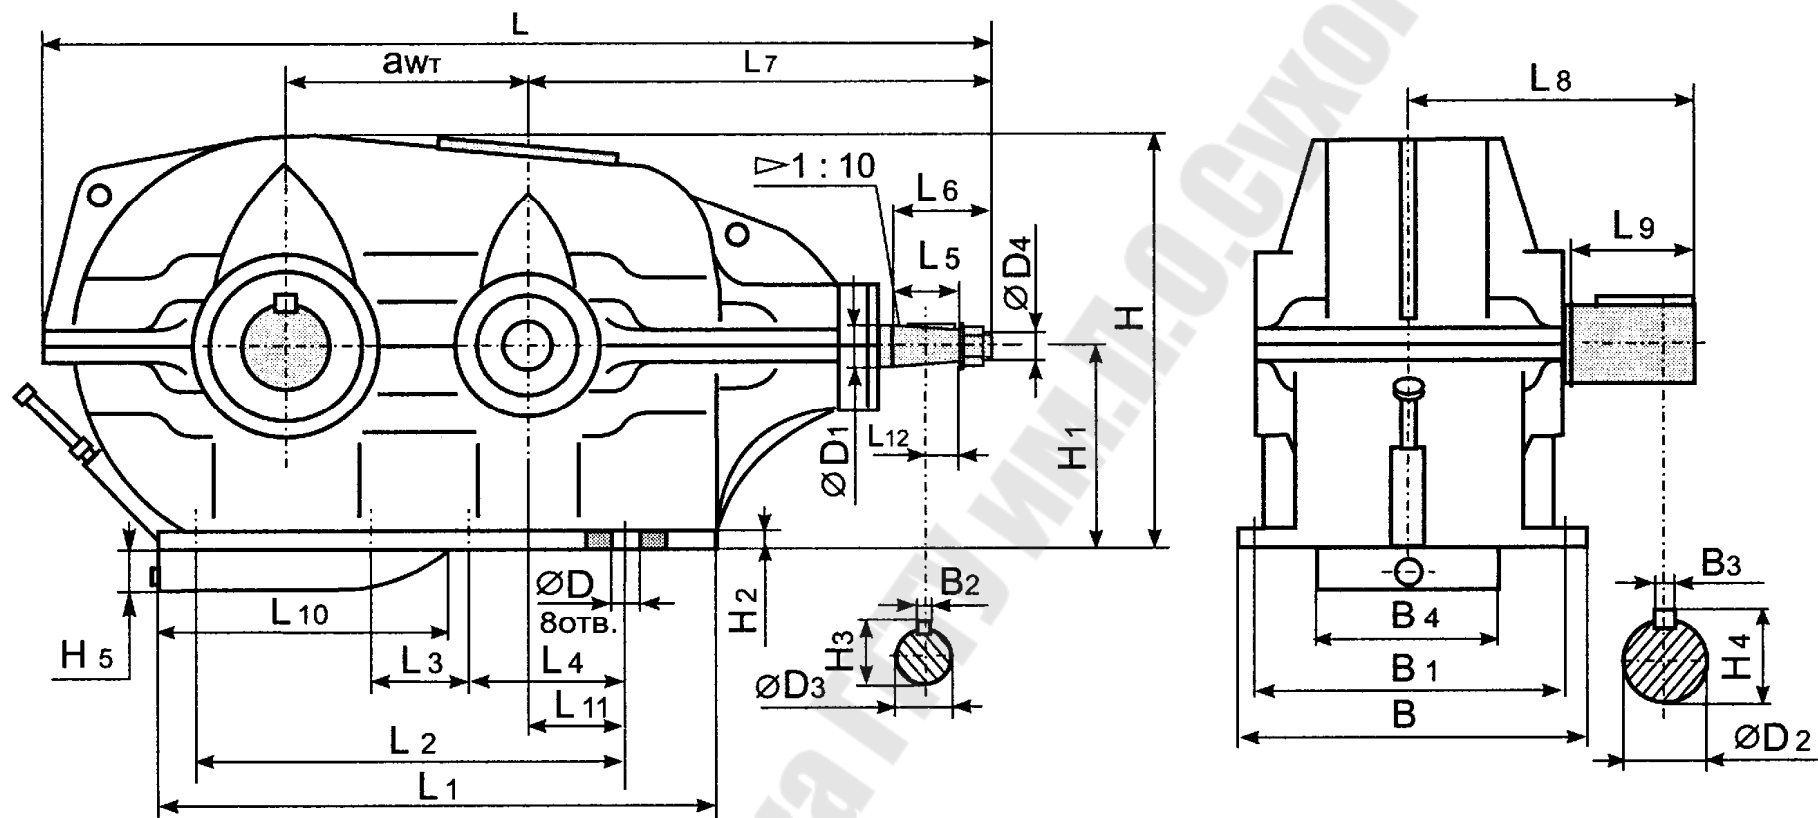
Редуктор коническо – цилиндрический двухступенчатый
